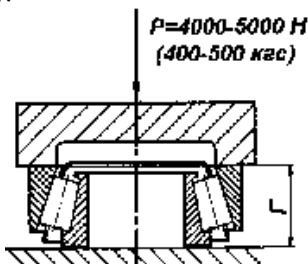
Замер монтажной высоты подшипника ведущей шестерни главной передачи
